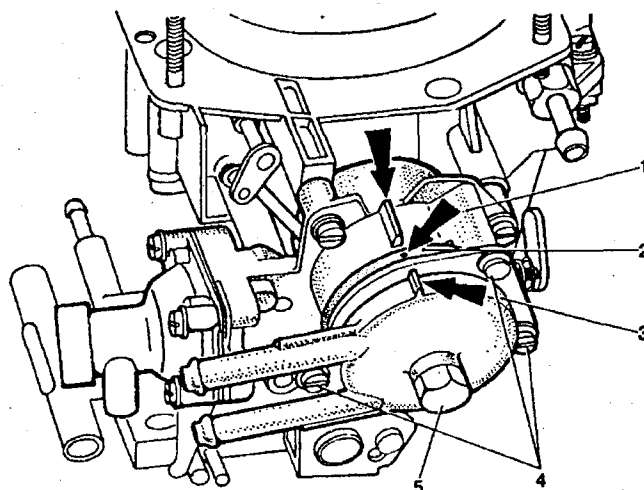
Проверка установки биметаллической пружины полуавтоматического пускового устройства карбюратора: 1 – корпус пускового устройства; 2 – корпус биметаллической пружины; 3 – корпус жидкостной камеры; 4 – винты крепления корпуса биметаллической пружины; 5 – болт крепления жидкостной камеры. Стрелками указаны метки для установки биметаллической пружины
